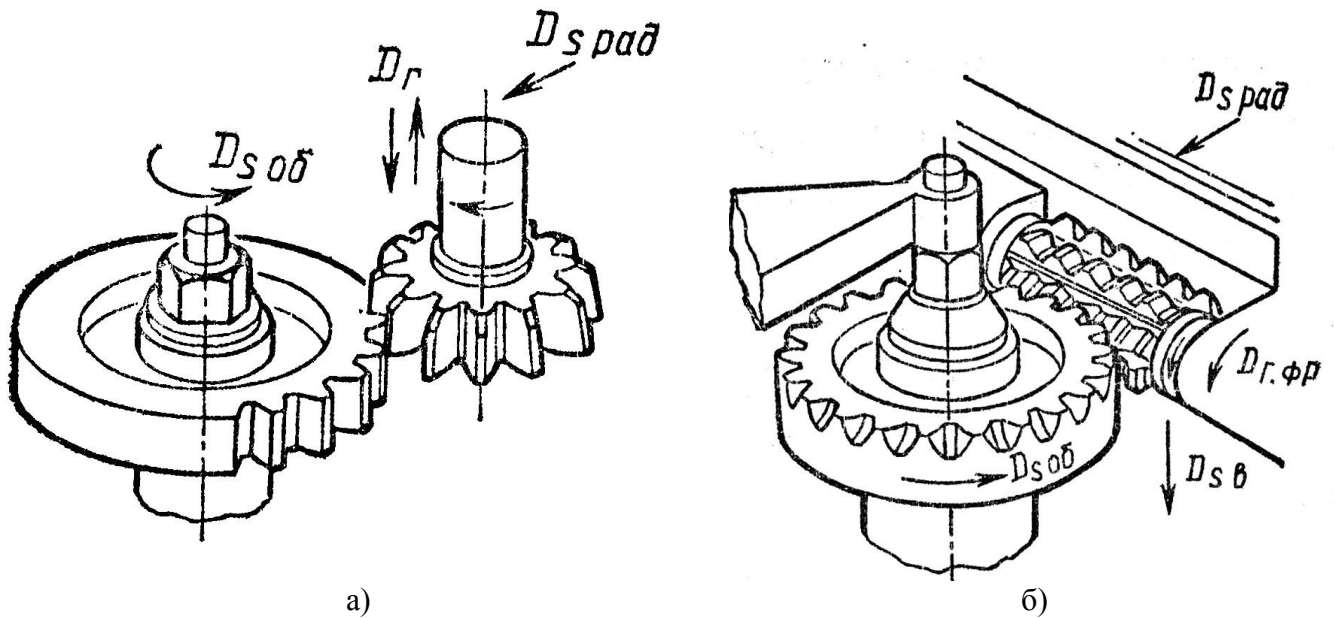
Схемы обработки зубчатых колес зуборезным долбяком (а) и червячной модульной фрезой (б):
